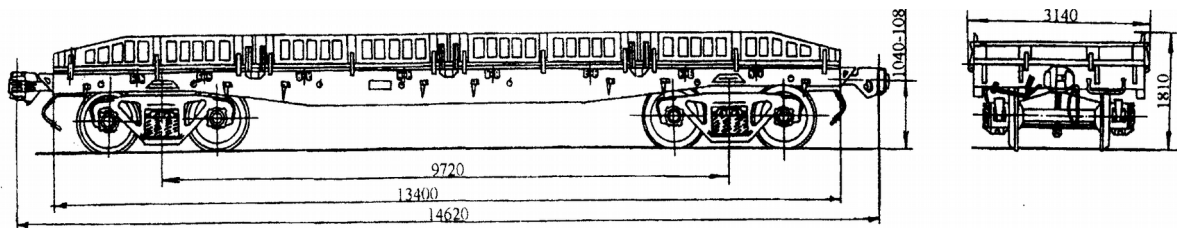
Ескіз чотиривісної платформи з металевими бортами, модель 13-Н451 (вигляд збоку і з торця)
